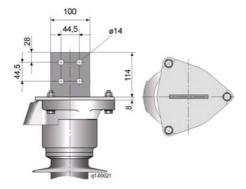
Conexión de alta tensión con terminal plano (NEMA)
